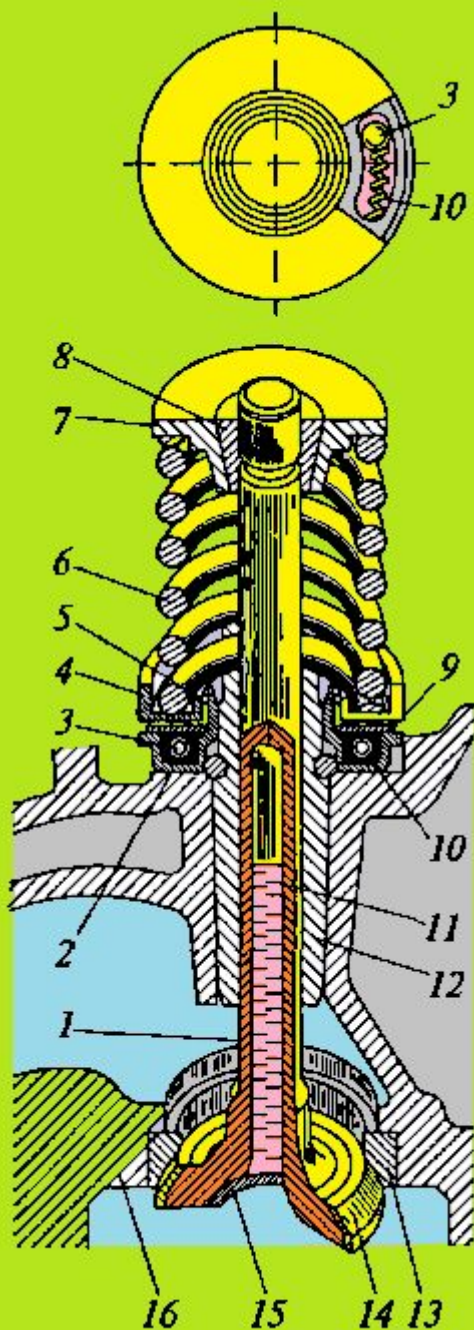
в. Газораспределительный механизм с верхним расположением клапанов и распределительного вала
